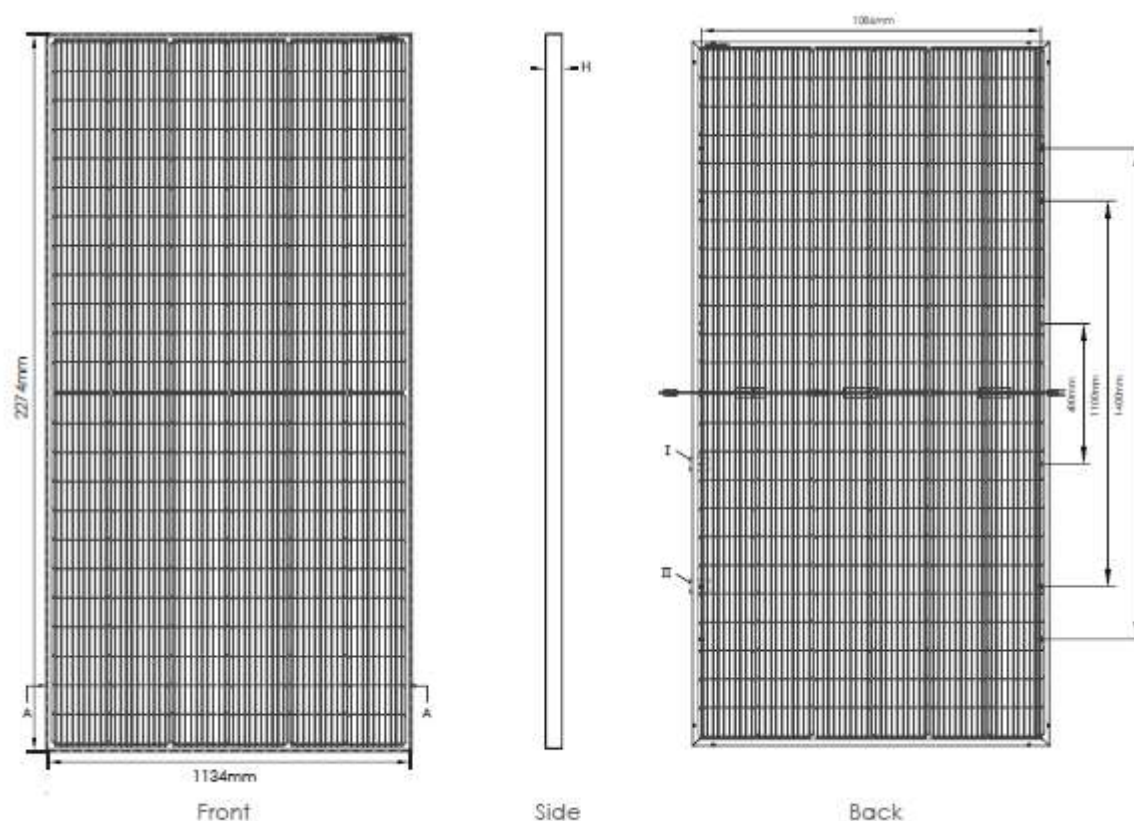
Dimensions et vue d'un panneau photovoltaïque de face
